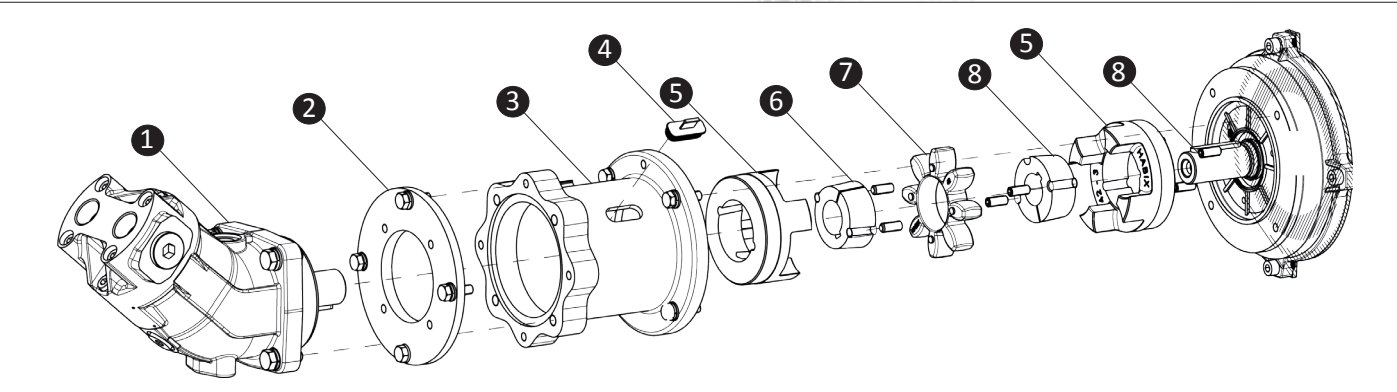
| Explosion embrague „BELL CLUTCH“
